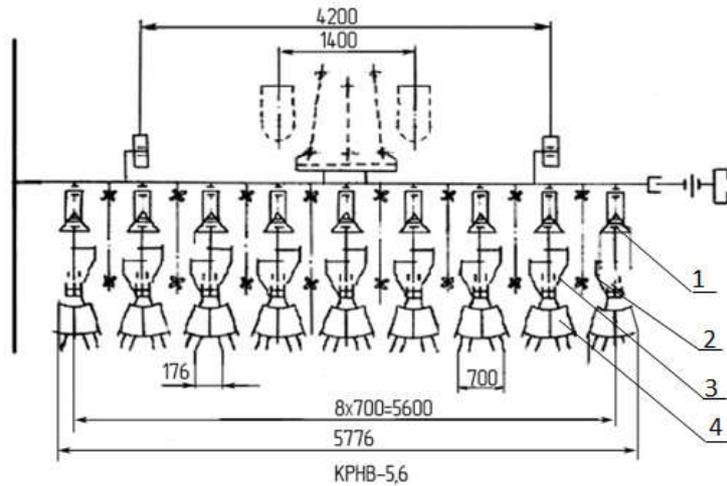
Схема розташування робочих органів під час роботи з борінками прополувальними для міжрядь 70 см:
